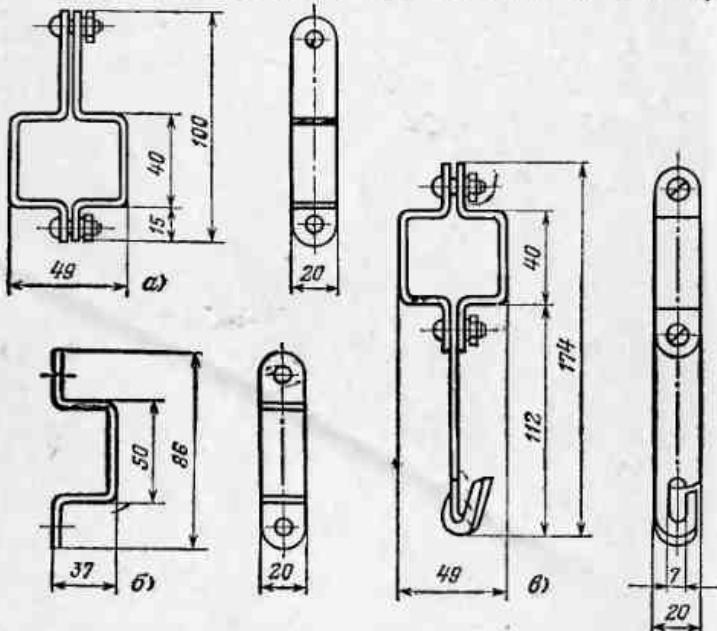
Опорные конструкции для крепления осветительных шинопроводов ШОС67.
